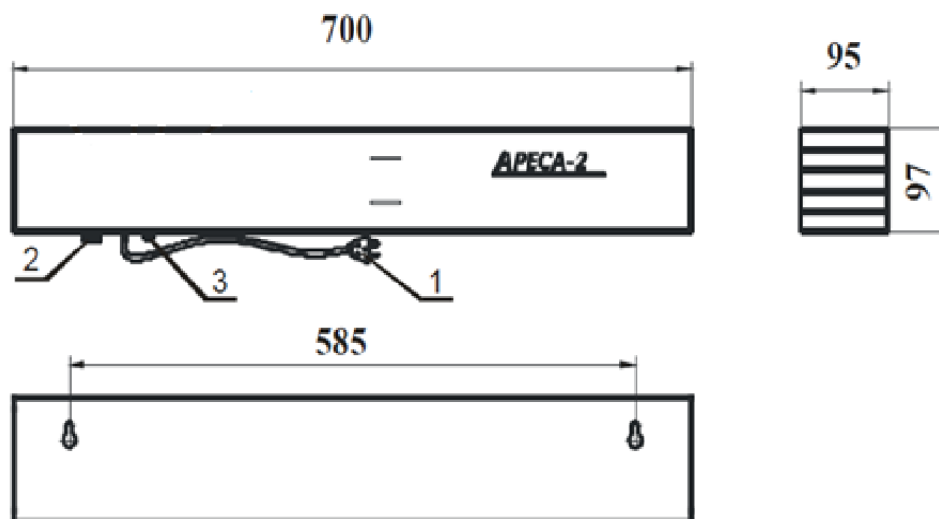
Внешний вид рециркулятора АРЕСА-2.
